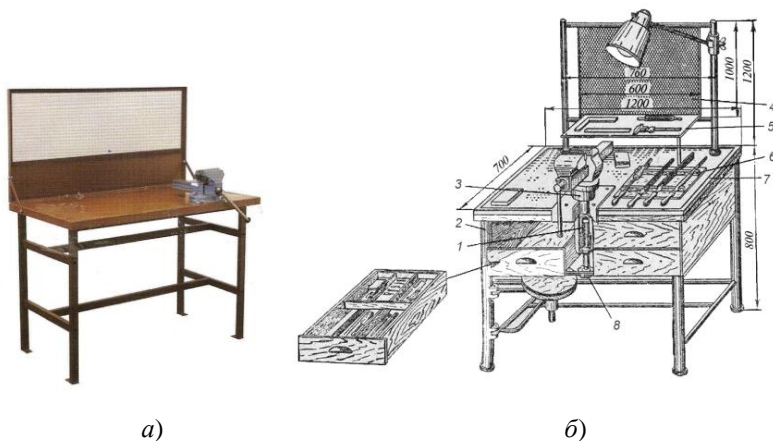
Слесарный верстак сварной конструкции с нерегулируемыми (а) и с регулируемыми по высоте тисками (б): 1 – винт подъема; 2 – каркас; 3 – труба; 4 – сетка; 5 – полочка; 6 – планшет; 7 – рамка; 8 – маховичок
